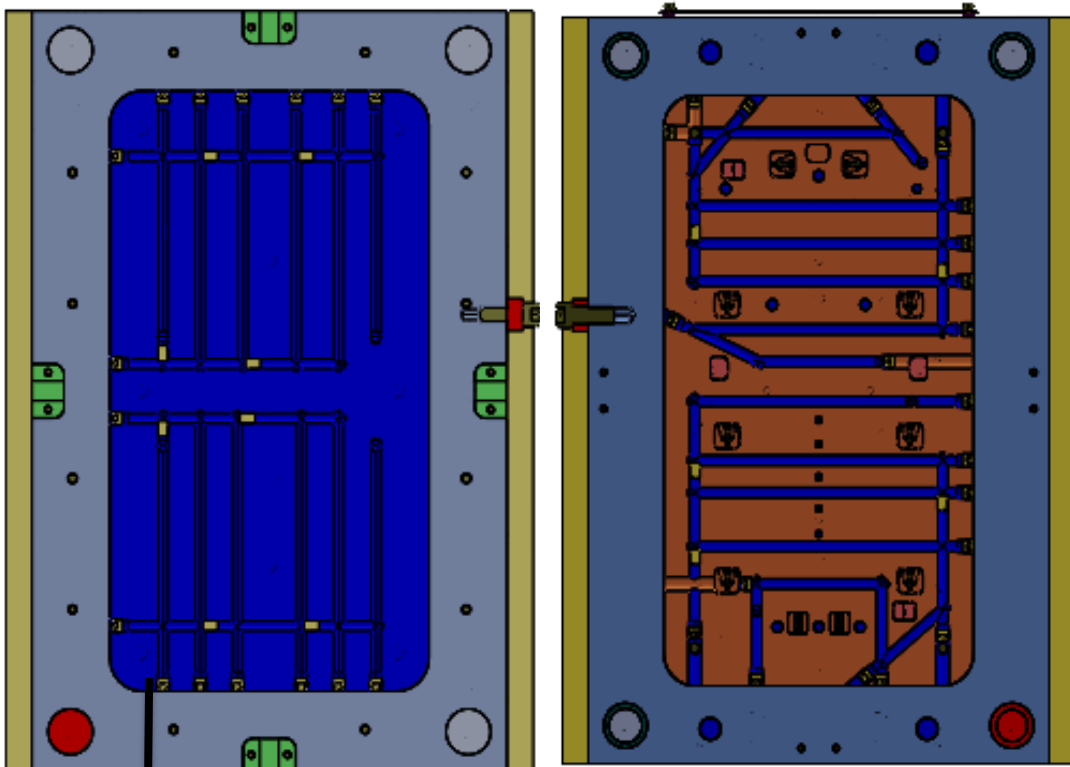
Sistemas de arrefecimento do lado de injeção do molde
